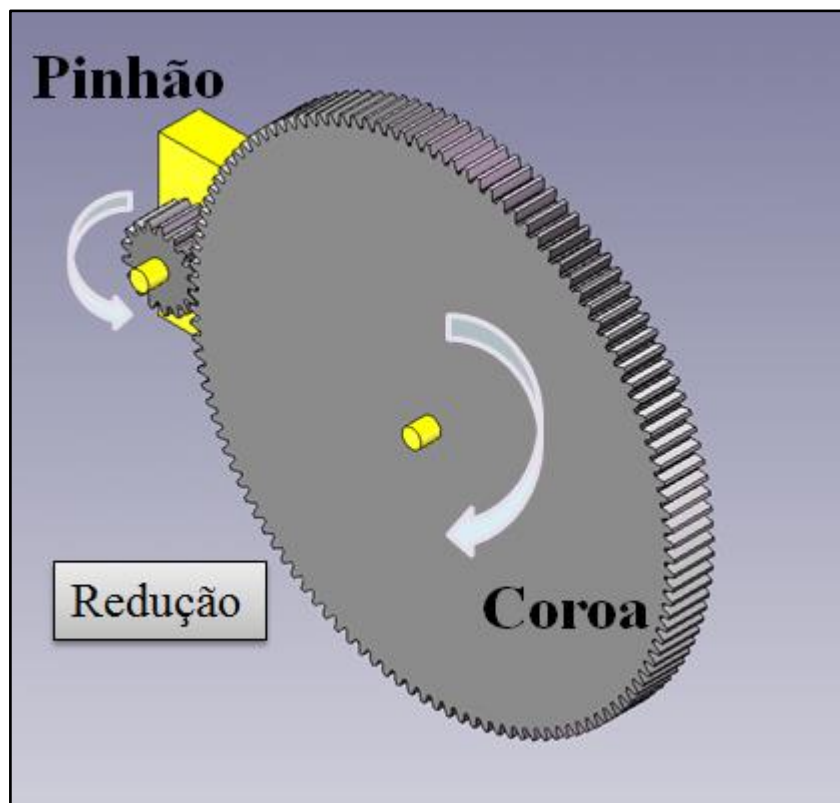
Máquina simples – Engrenagens – Pinhão e coroa.
